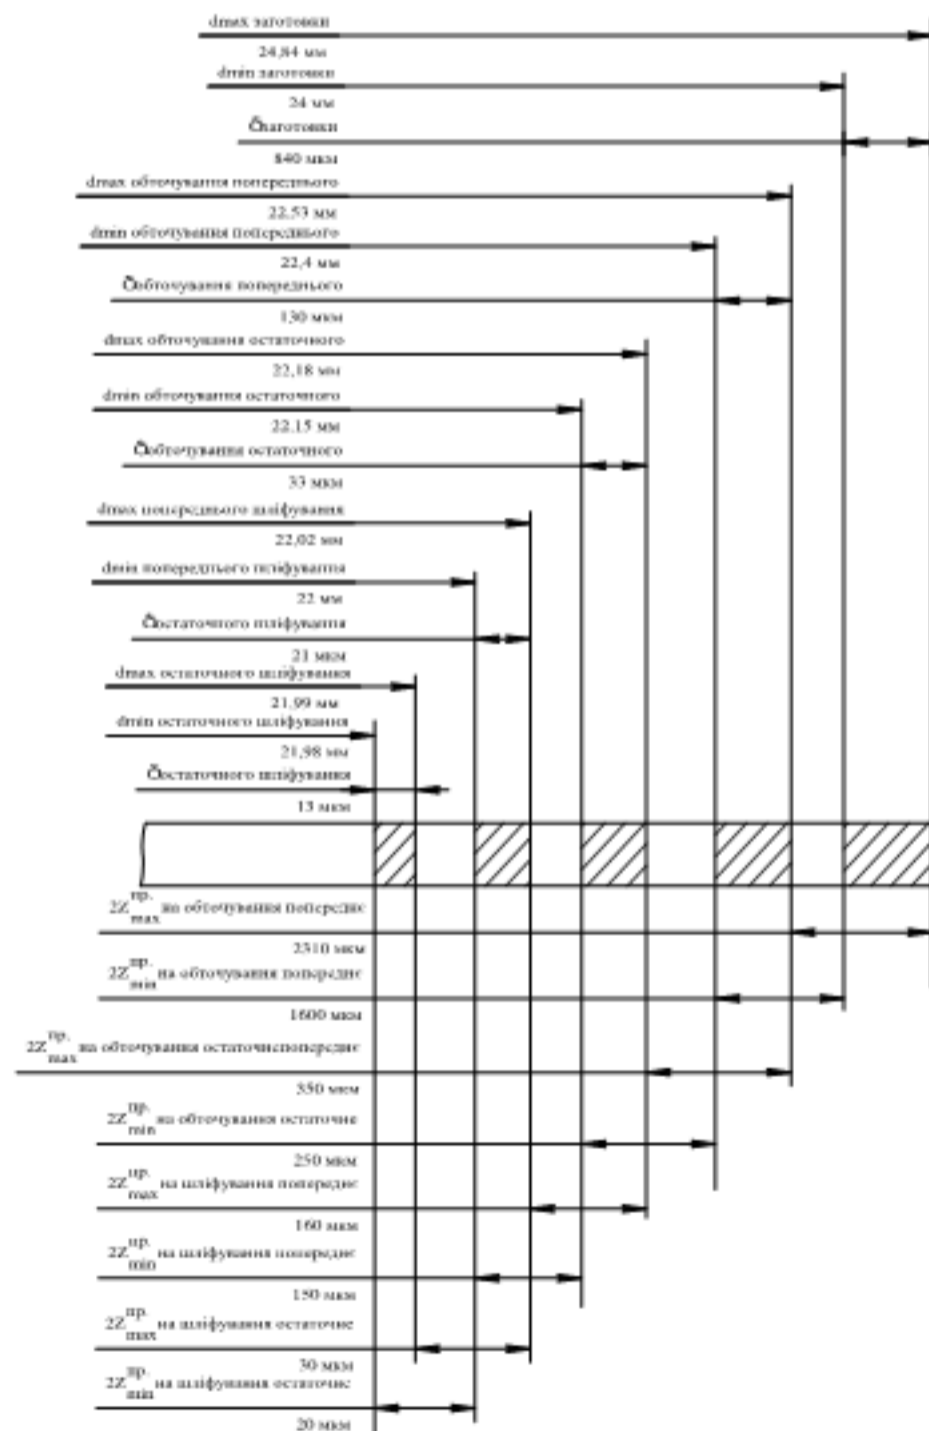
Схема графічного розташування припусків та допусків на обробку пов. Ø22g6
